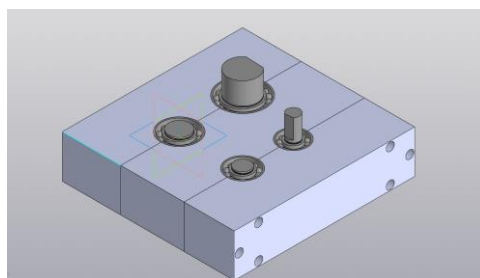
Корпус и подшипники в системе Компас 3D
